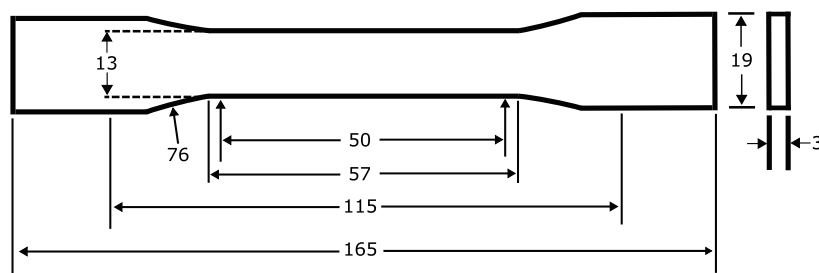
Dimensiones de probeta de tracción uniaxial de la norma ASTM D638-14.
